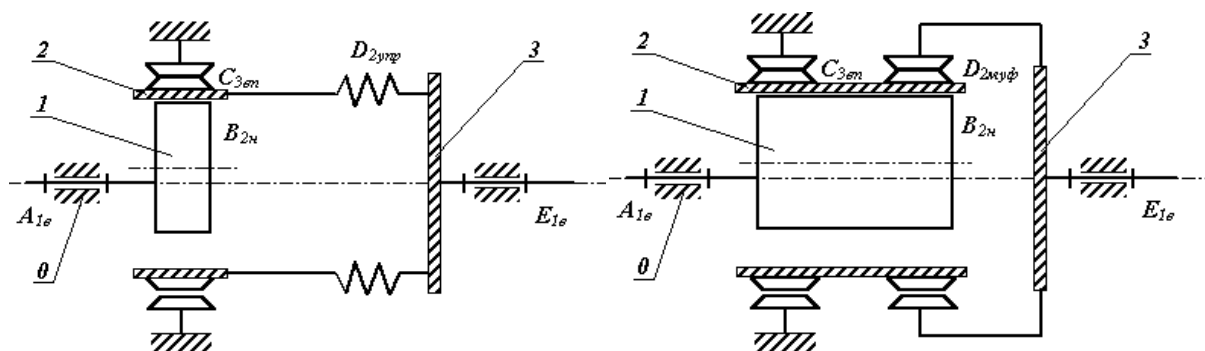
Волновая зубчатая передача с упругой муфтой - стаканом (Левый рис.). Волновая зубчатая передача с волновой зубчатой муфтой (Правый рис.).
